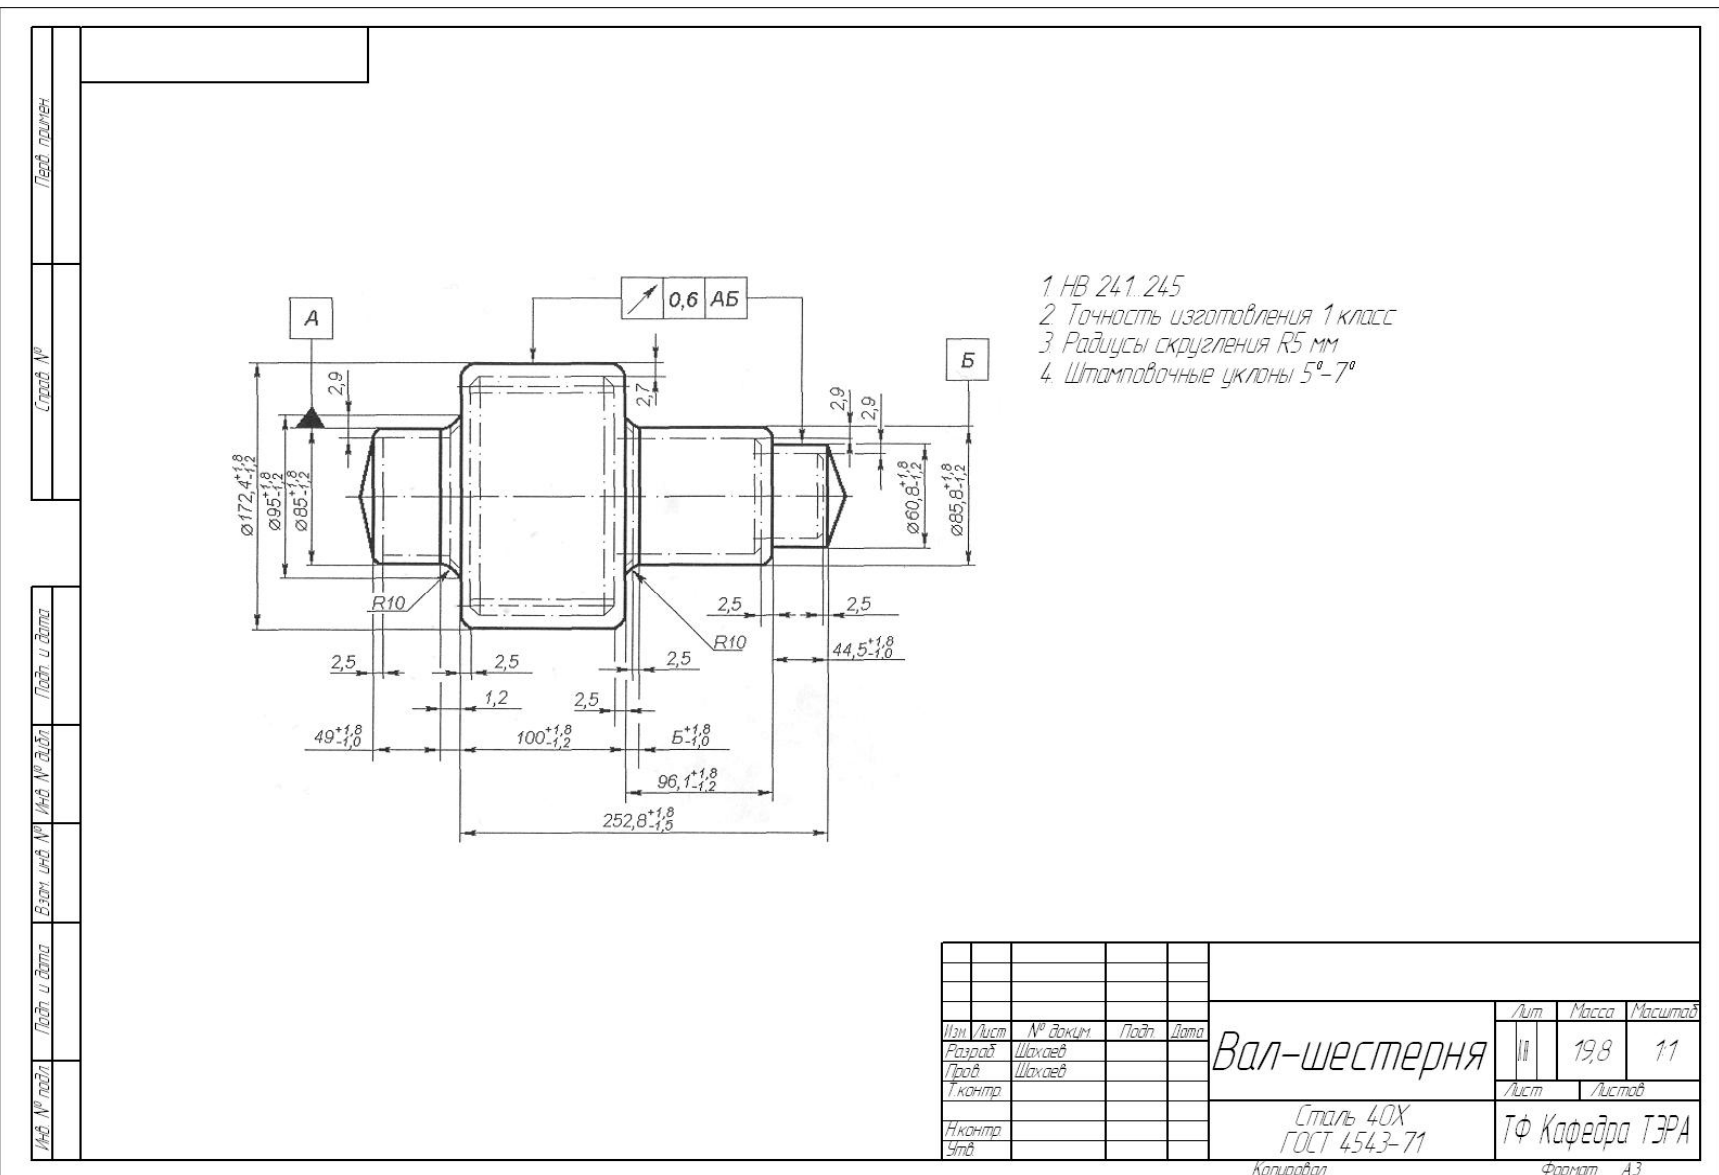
Пример оформления чертежа заготовки (вала-шестерни)
